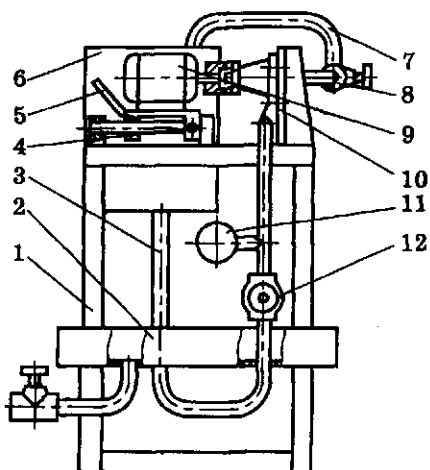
Стенд для испытания водяных насосов: 1 — корпус; 2 — емкость; 3 — патрубок нагнетательный; 4 — болт; 5 — рукоятка; 6 — бак для воды; 7 — патрубок всасывающий; 8 и 12 — вентили; 9 — электродвигатель; 10 — установочная плита; 11 — манометр
